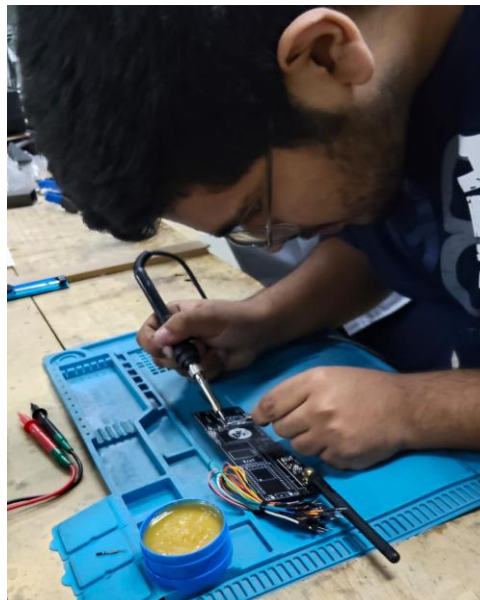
Soldadura de la PCB y pruebas electricas
